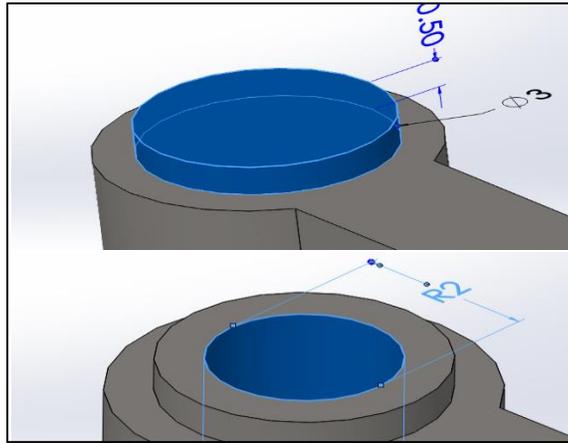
Detallado de la biela para unión con pistón. Fuente: Diseño propio.
